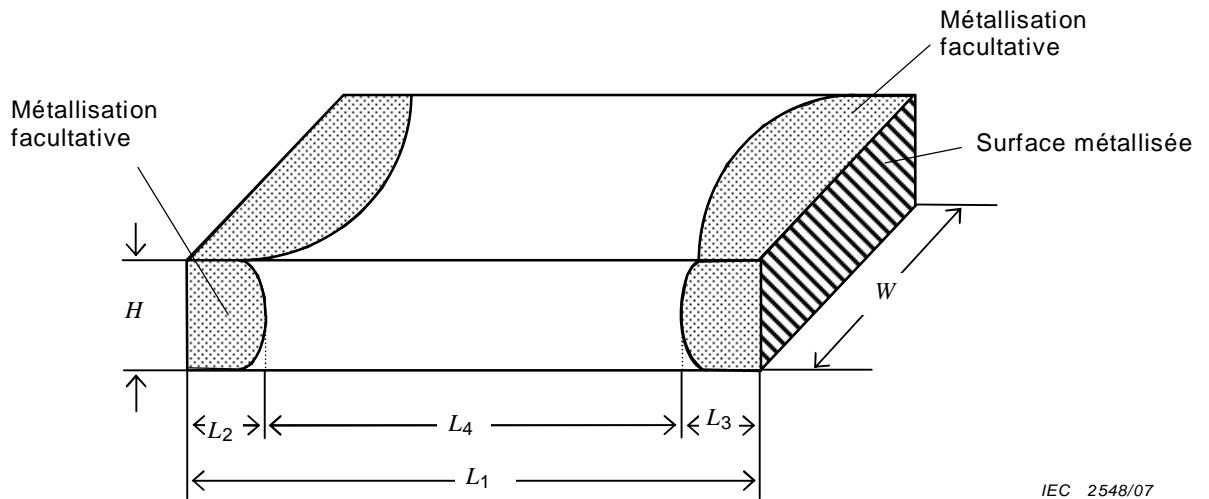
Dimensionnement des thermistances pour montage en surface
